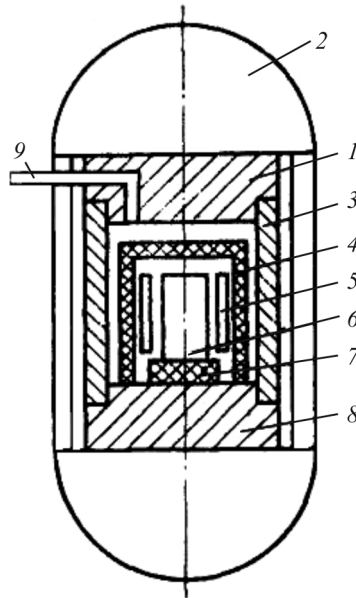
Схема высокотемпературного газостата, используемого для диффузионной сварки: 1 – верхняя пробка; 2 – станина; 3 – контейнер; 4 – термоизоляционный колпак; 5 – нагреватель; 6 – свариваемая деталь; 7 – термоизолятор; 8 – нижняя пробка; 9 – трубопровод подачи рабочего газа
